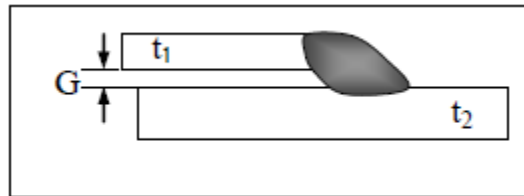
Ejemplo de medición del gap. Fotografía extraída de la especificación general de Ford sobre soldadura MAG ESBM5A-1B310-AA.
